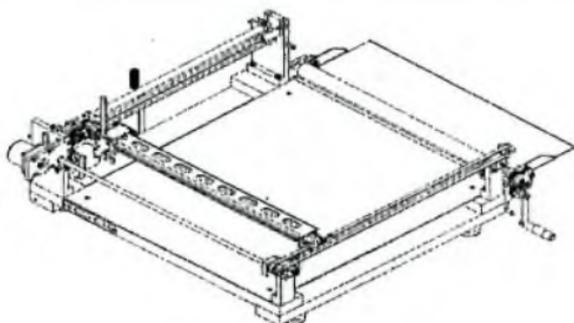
Общий вид стенда (без защитных кожухов)
